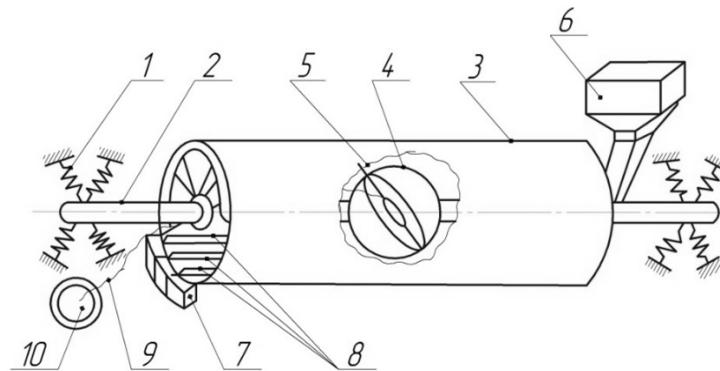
Принципова схема сепаратора з циліндричною робочою поверхнею
